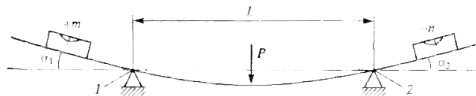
Прогиб вала: 1 и 2 — подшипники; 3 — уровень.
